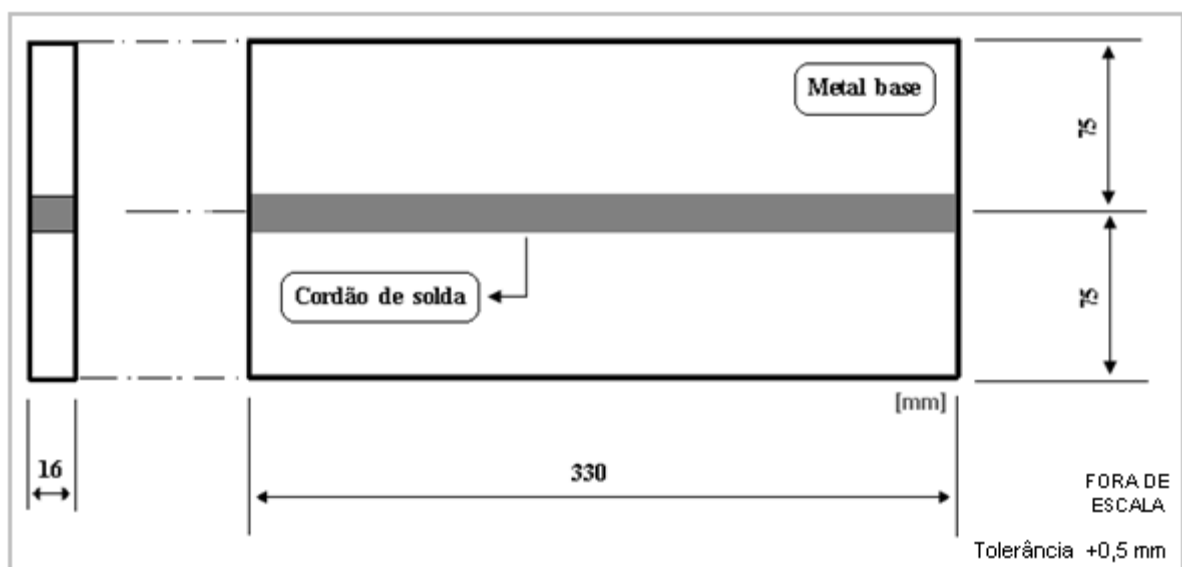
Detalhe ilustrativo das chapas soldadas.
